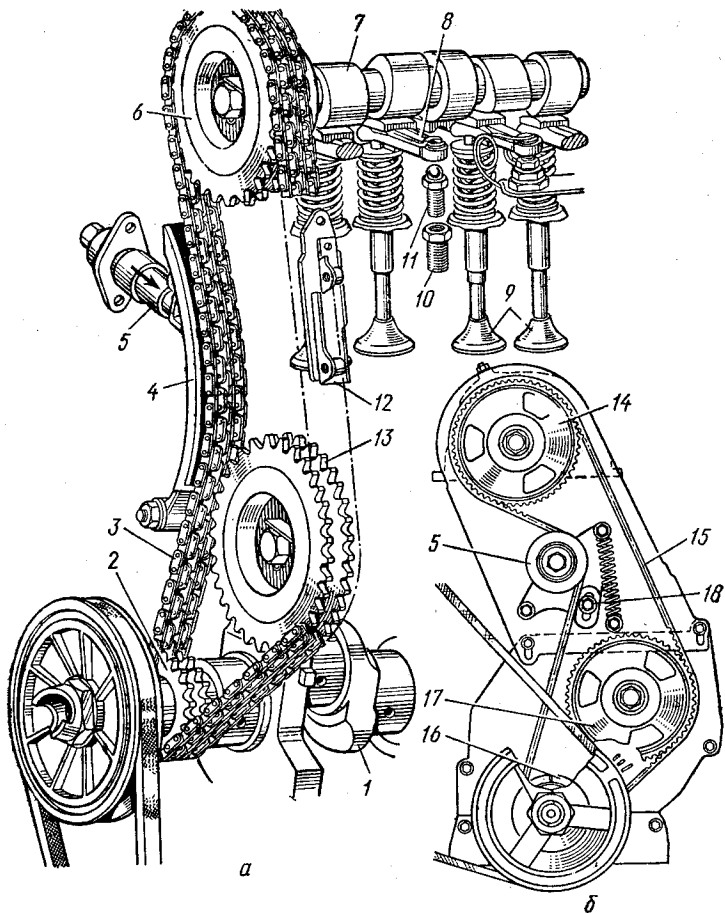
Привод механізму газорозподілу з верхнім розташуванням розподільного вала:
